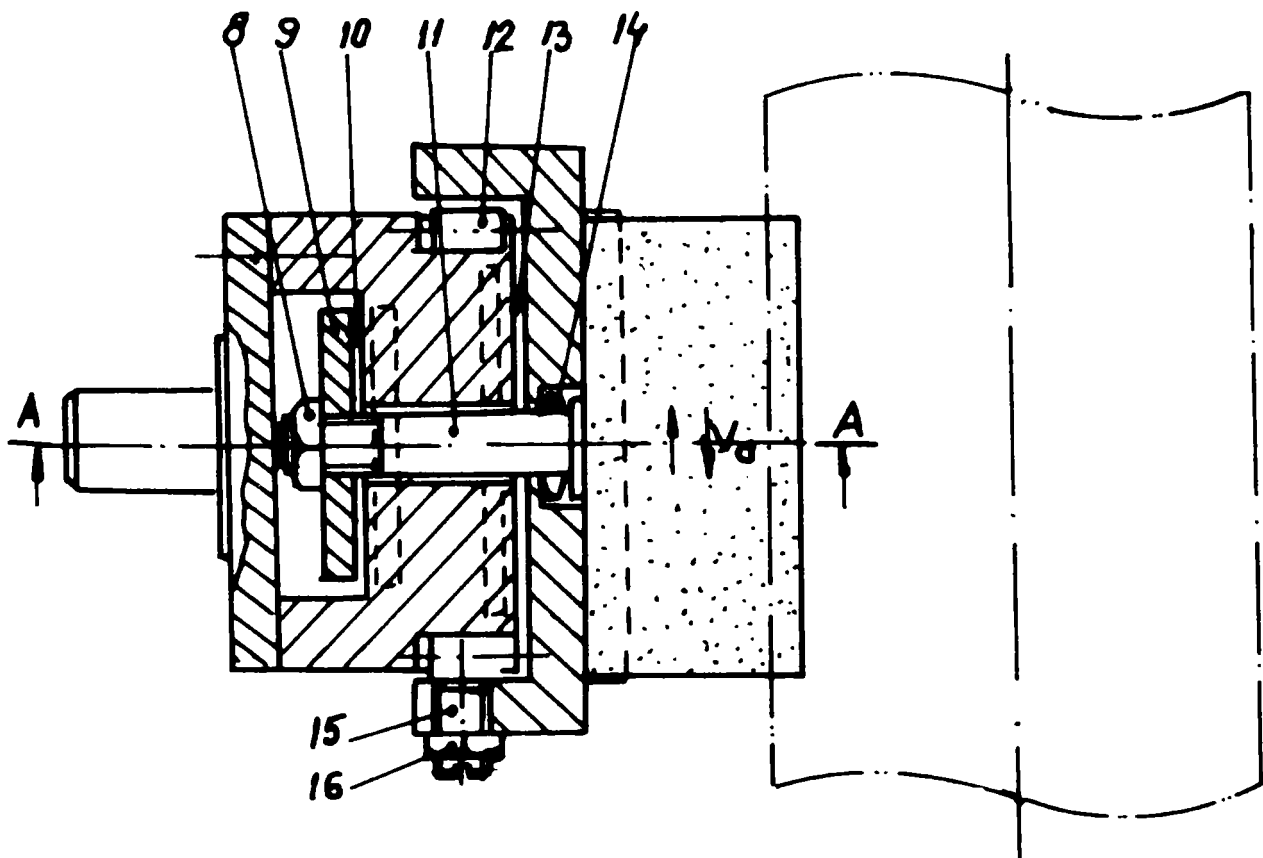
Schema constructivă a elementului traductor pentru măsurarea forței de așchiere tangențiale
